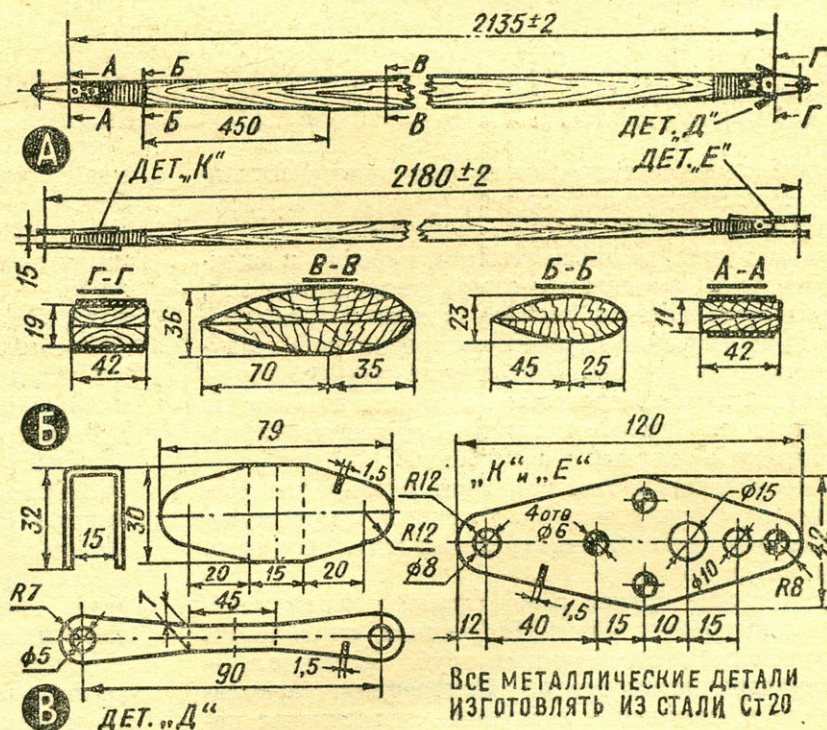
Конструкция подкоса крыла и детали: А — основные размеры; Б — сечения; В — металлические детали.
